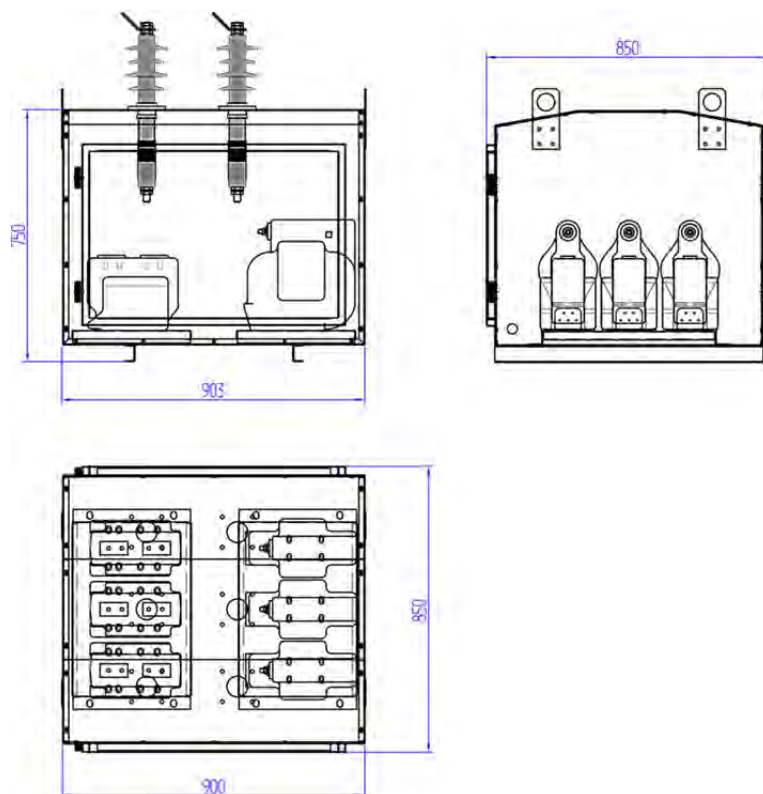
Высоковольтный шкаф. Общий вид и габаритные размеры
